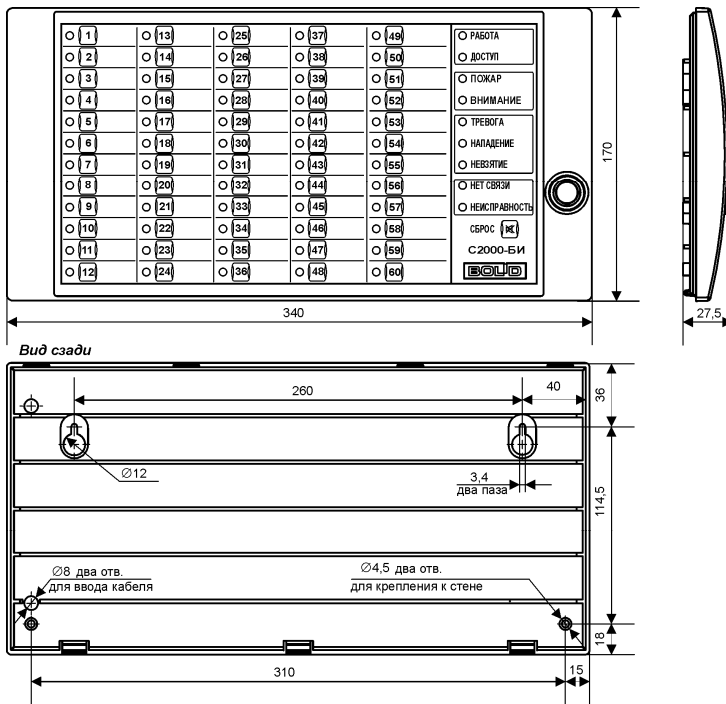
Внешний вид, габаритные и установочные размеры блока
